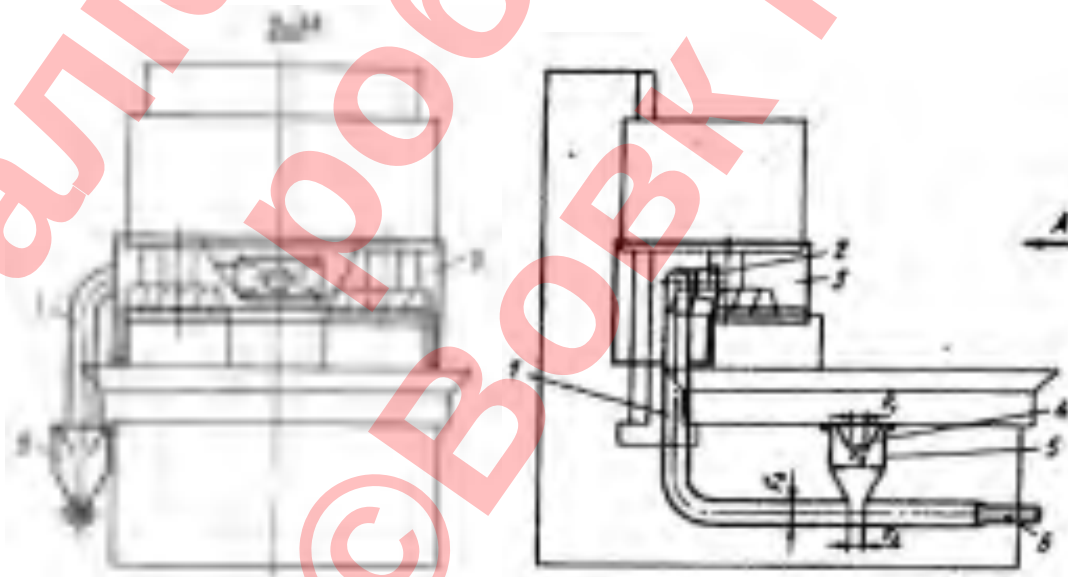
Схема пристрою для видалення пилу і стружки 1281376
